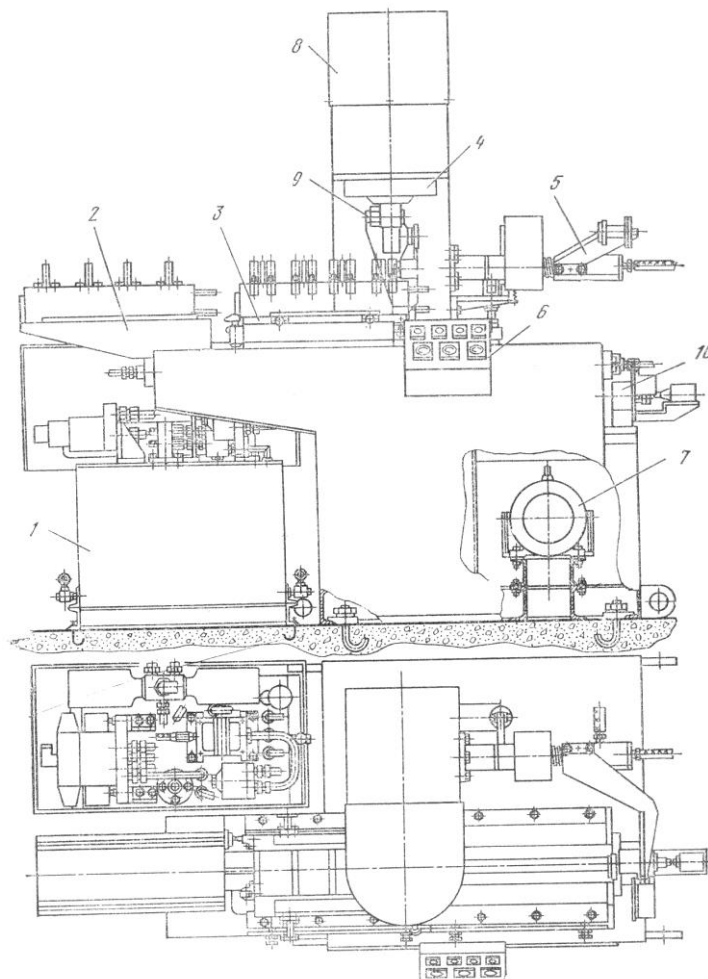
Стенд для перепресовки втулок ГБЦ, модель HP-7302/5
